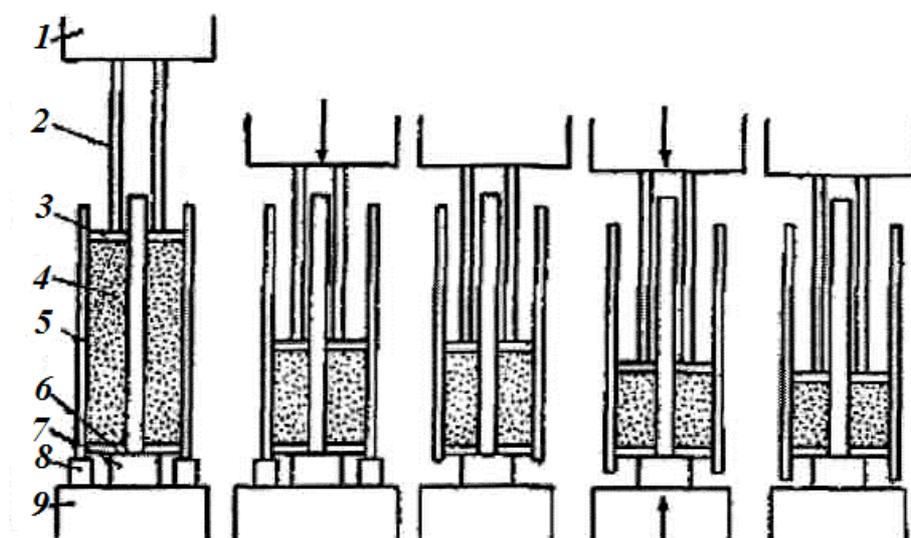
Схема формирования заготовки двусторонним прессованием (с плавающей матрицей):
